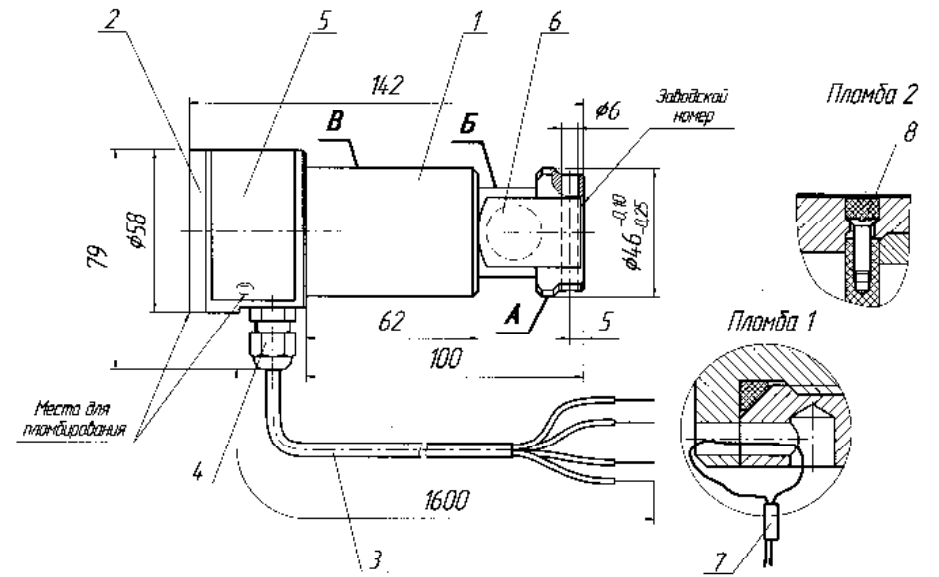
Корпус тип 1. Габаритные и присоединительные размеры.
